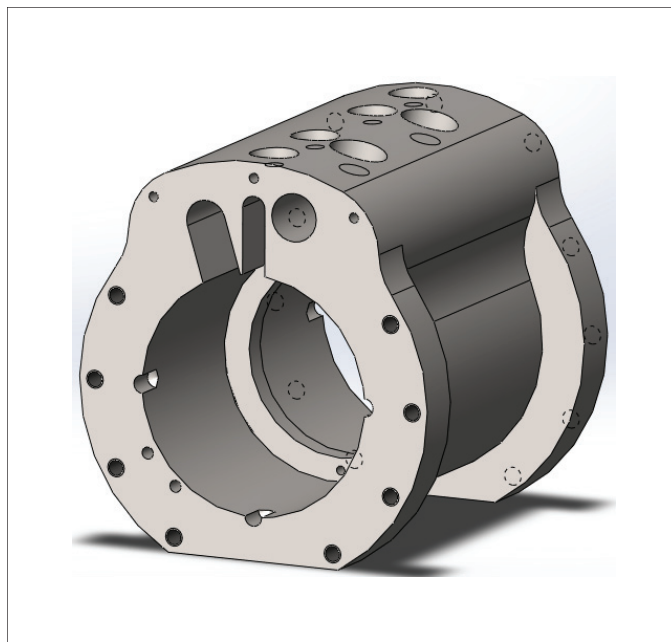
Корпус роторного компрессора с катящимся ротором транспортной холодильной установки
